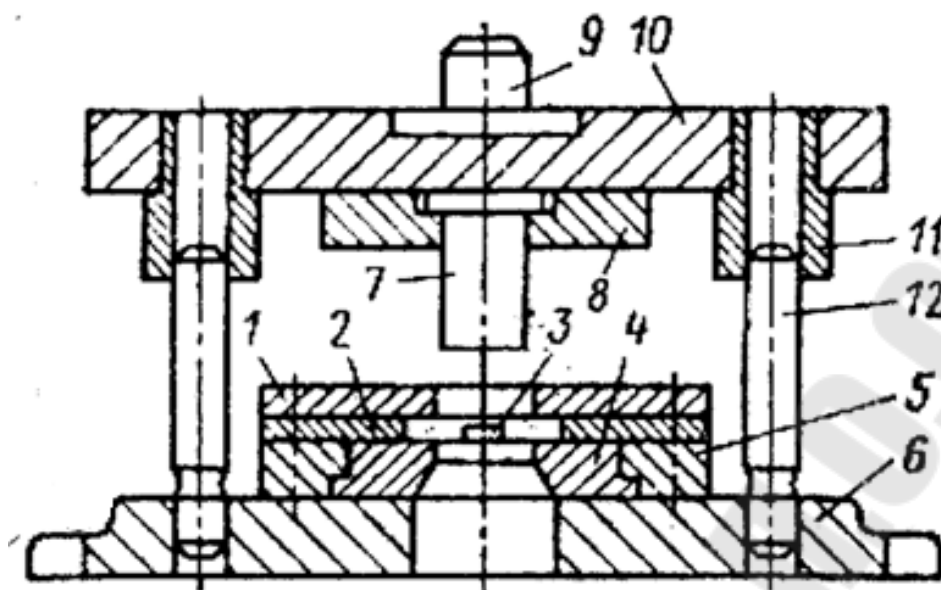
Схема вырубного штампа: 1 - съемник; 2 - направляющие линейки; 3 - упор; 4 - матрица; 5 - матрицедержатель; 6, 10 - нижняя и верхняя плиты; 7 - пуансон; 8 - пуансонодержатель; 9 - хвостовик; 11 - направляющие втулки; 12 - направляющие колонки
